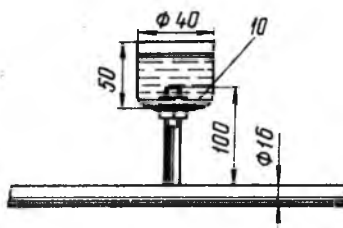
Схема установки патрубка со стаканом (10 — резиновая прокладка)
